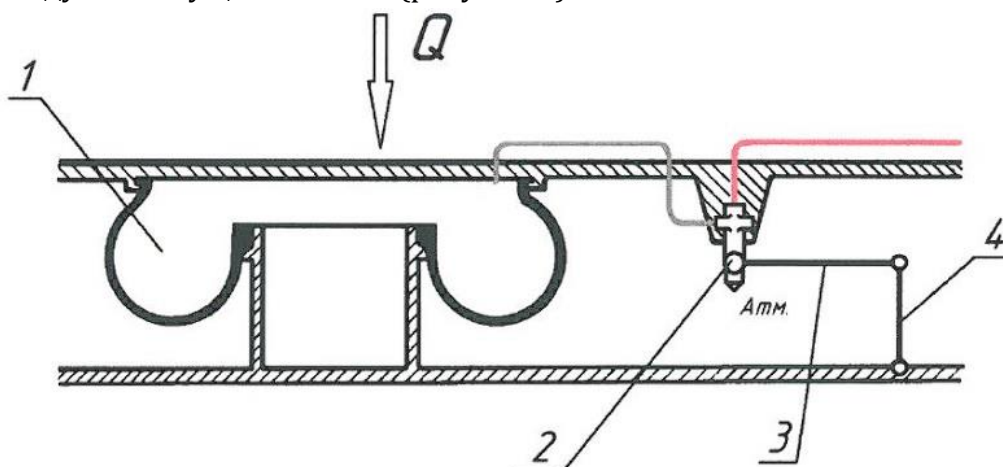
Система пневматической рессоры в уравновешенном положении: 1 - пневматическая рессора; 2 - впускной клапан; 3 - рычаг управления клапана; 4 - тяга управления; Q - нагрузка.
